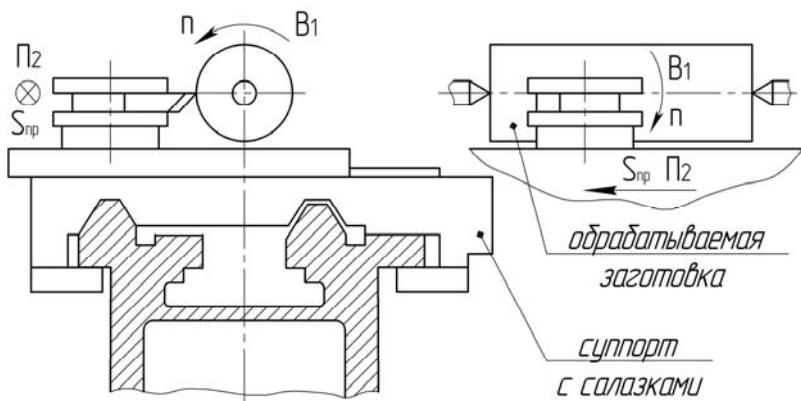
Рабочая зона токарно-винторезного станка и формообразующие движения при обработке цилиндрической поверхности с продольной подачей суппорта
